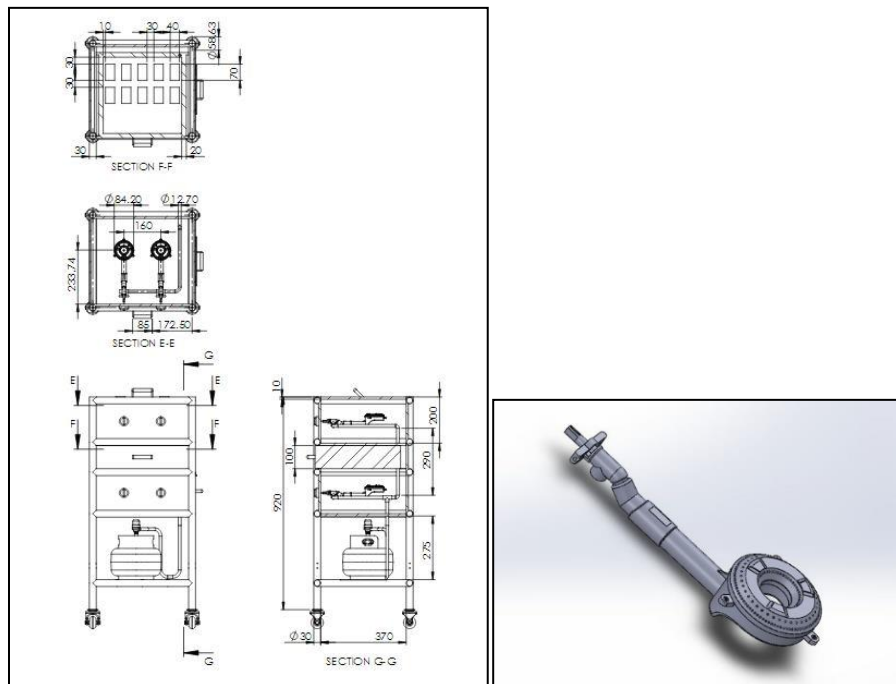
Alat Panggang Kue Balok Rancangan 2 Tampak Depan dan Tampak Atas
